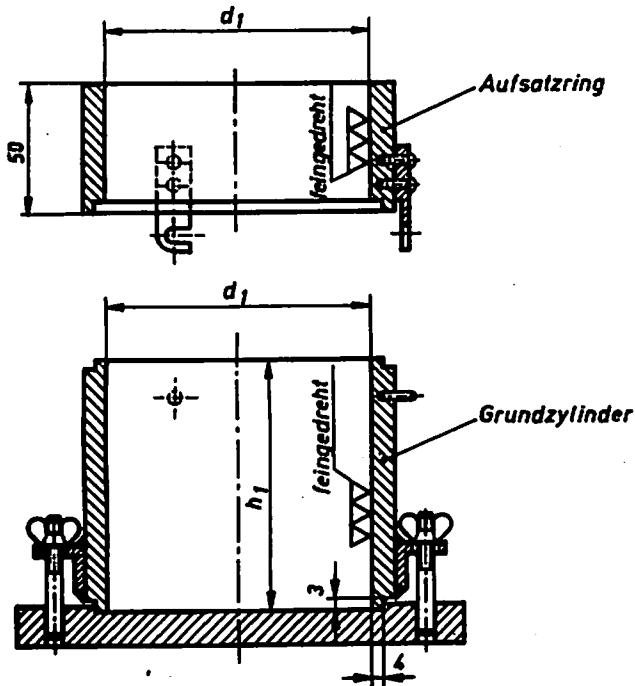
Standardverdichtungszyylinder mit angeschraubter Grundplatte
